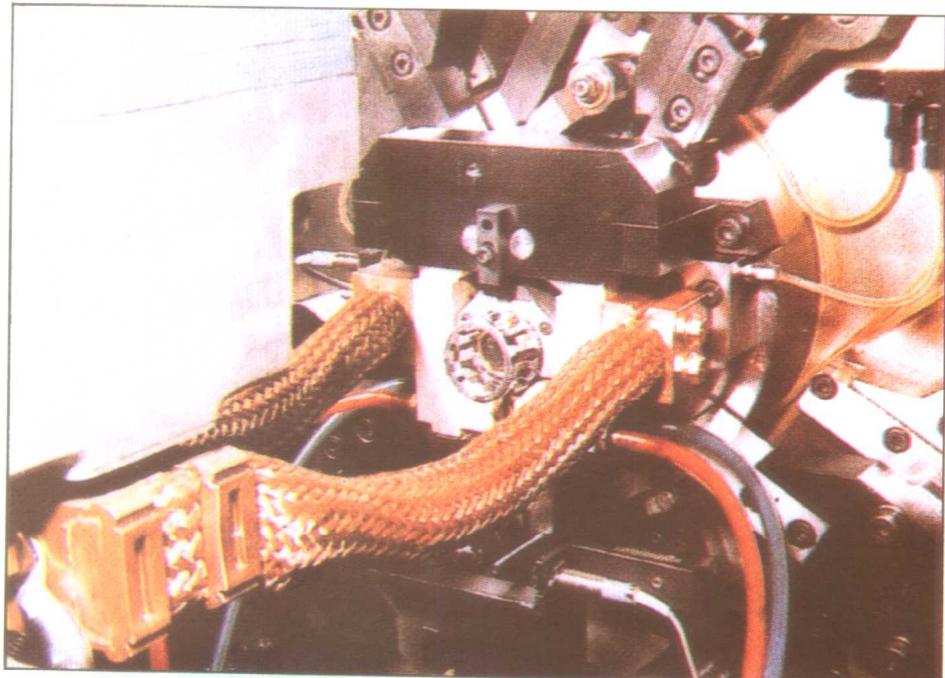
组合功能精密电阻焊机用于焊接微型轴承保持圈
